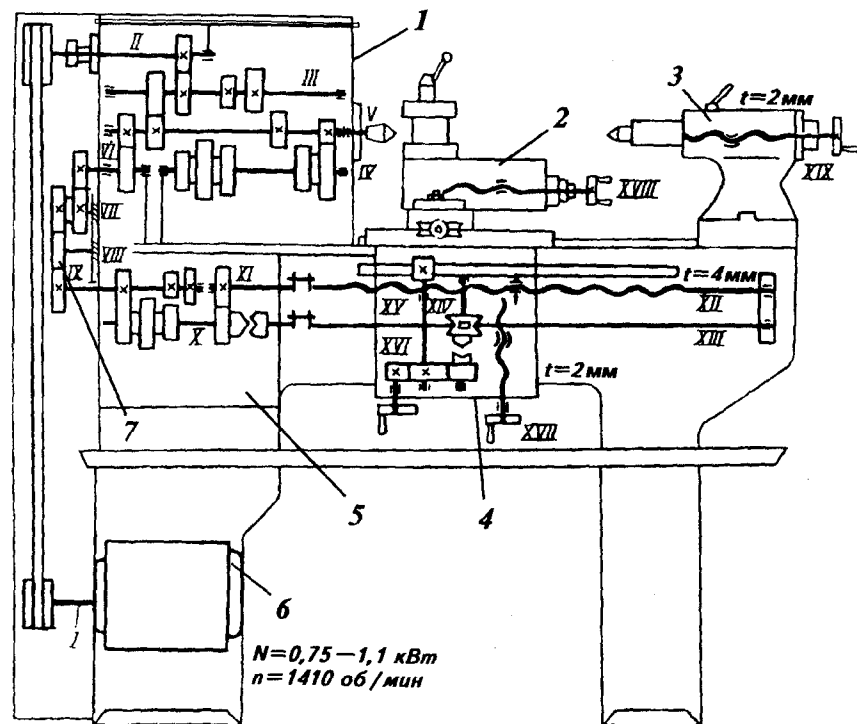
Кинематическая схема токарно-винторезного станка ТВ-6:
